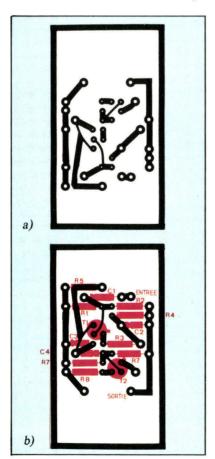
Circuit imprimé vu côté « soudures » (a) et côté composants (b).
